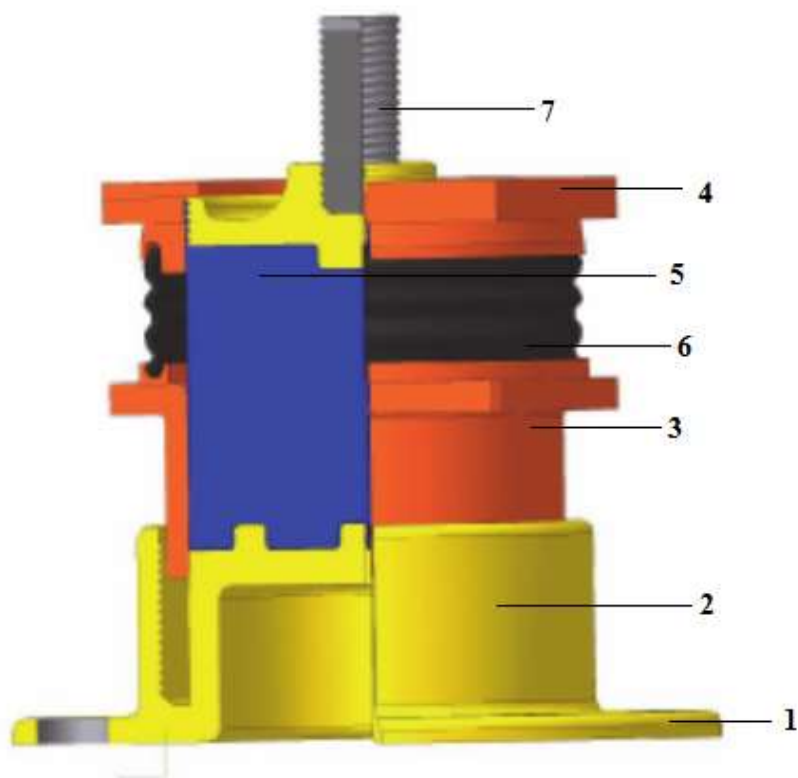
Виброизолирующая опора для компрессора. 1 – опорный фланец 2 – стакан-корпус 3 – регулятор 4 – платформа 5 –демпфер 6 –пыльник 7 – крепёжные элементы
